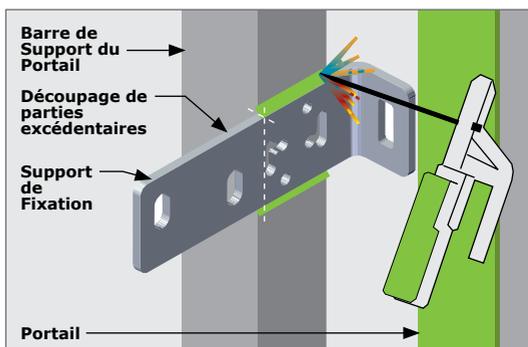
BARRE DE SUPPORT - SOUDÉE
